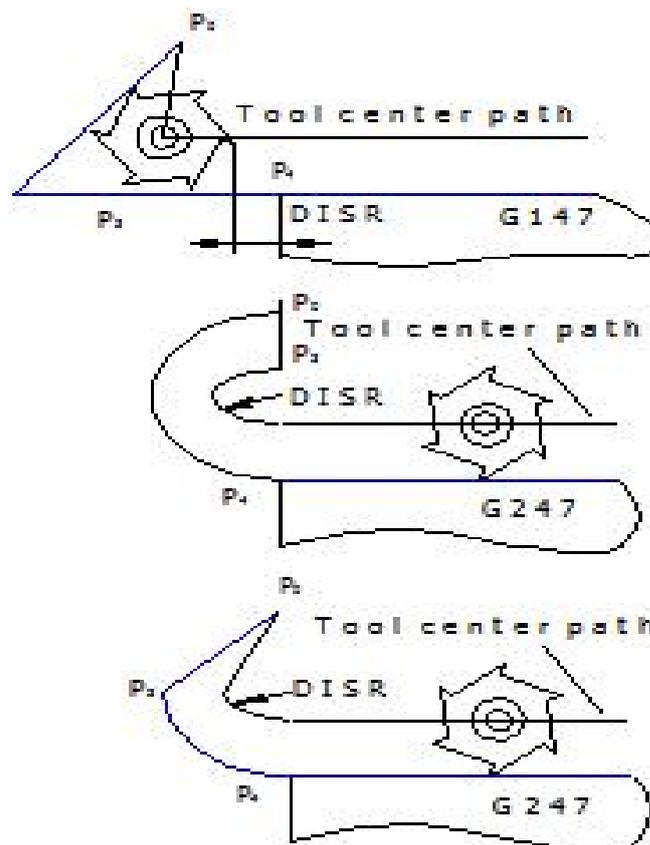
Подвод фрезы к заготовке по прямой линии и кругу
